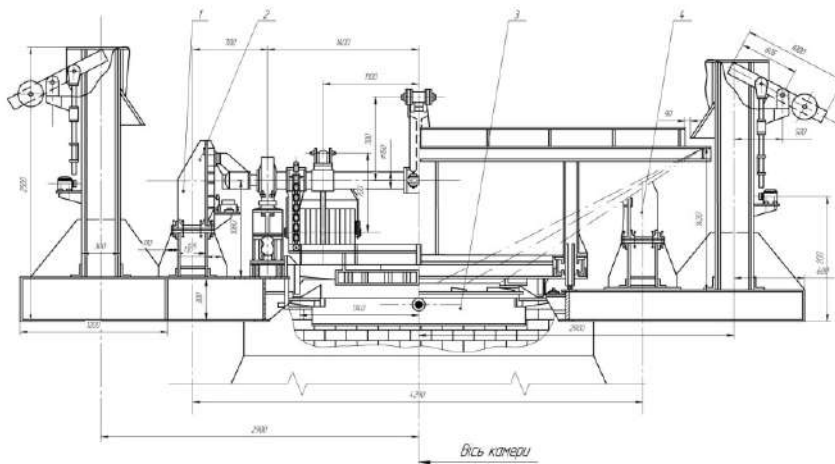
Механізм пересування платформи з кузовом (штанга пряма)
